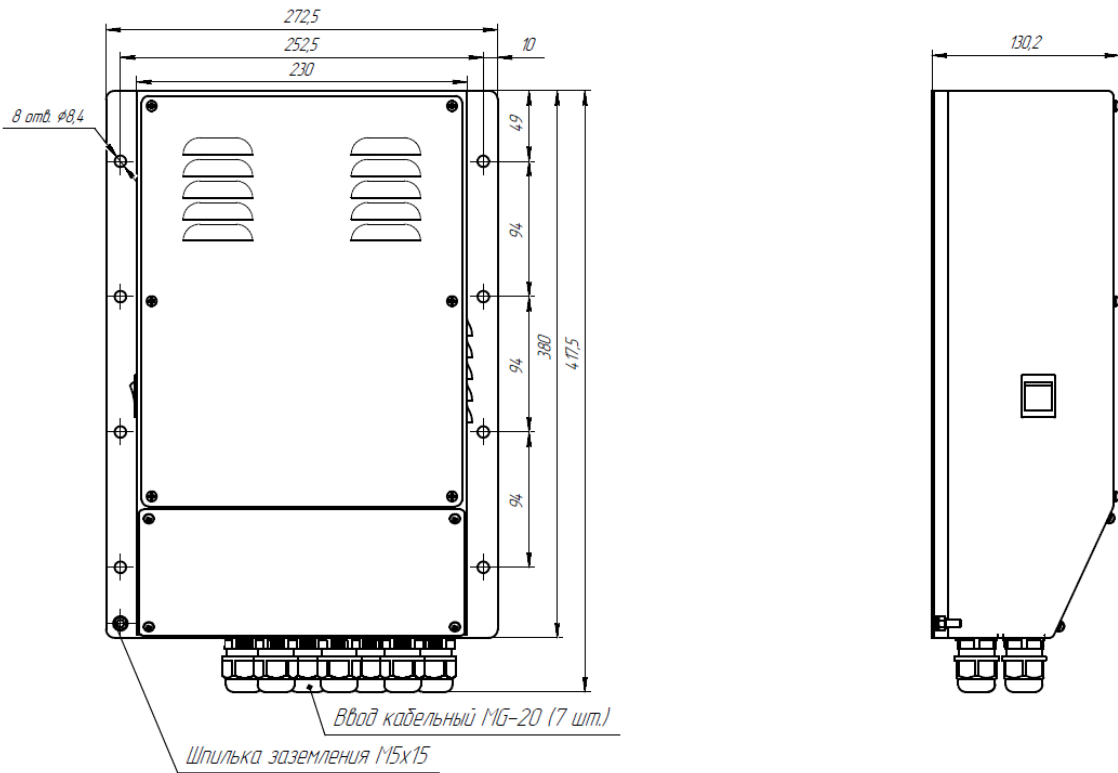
Габаритные и установочные размеры БП-103-20
